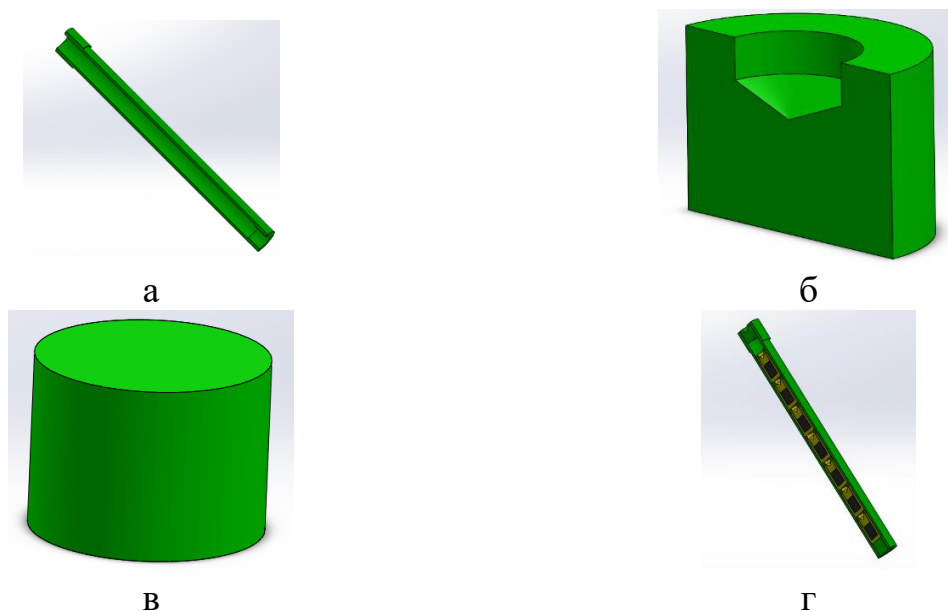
Канал с семью капсулами: а – корпус канала; б – верхняя крышка канала; в – нижняя крышка канала; г – канал с 7-ю капсулами в сборе
